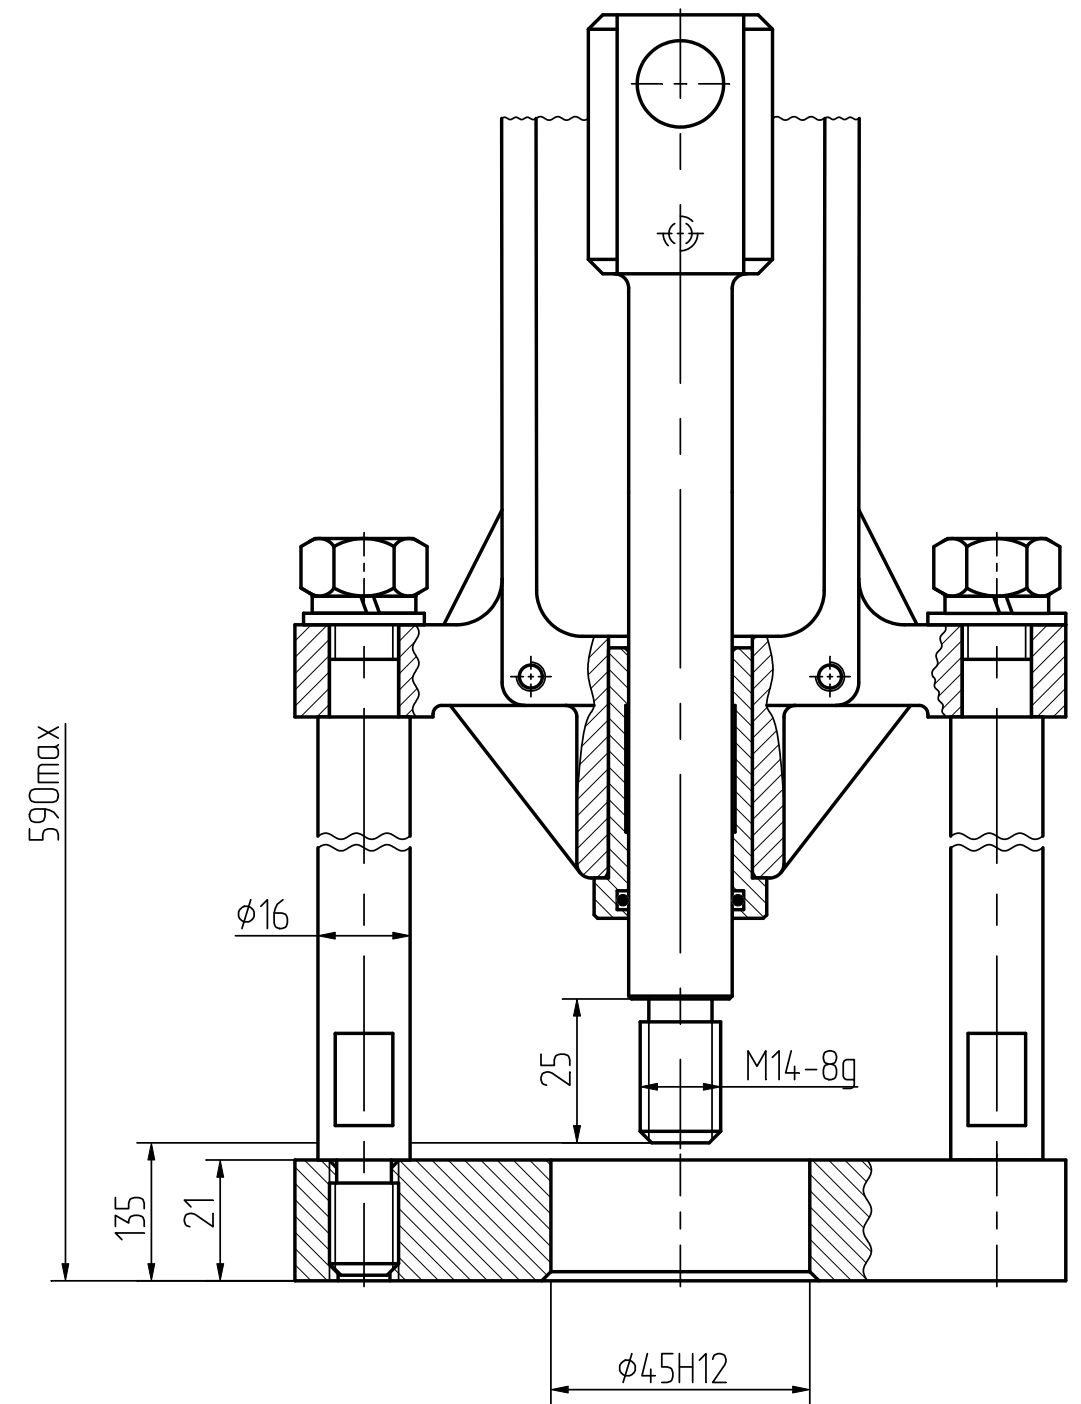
Общий вид, габаритные и присоединительные размеры МЭПК-6300-ИВТ4-03
